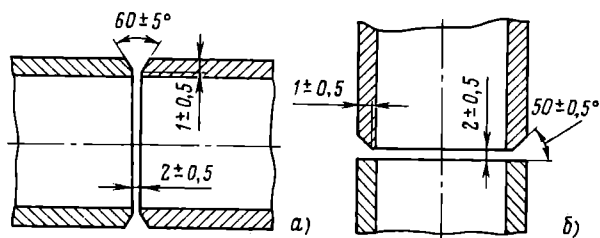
Подготовка концов экранных труб под сварку:
